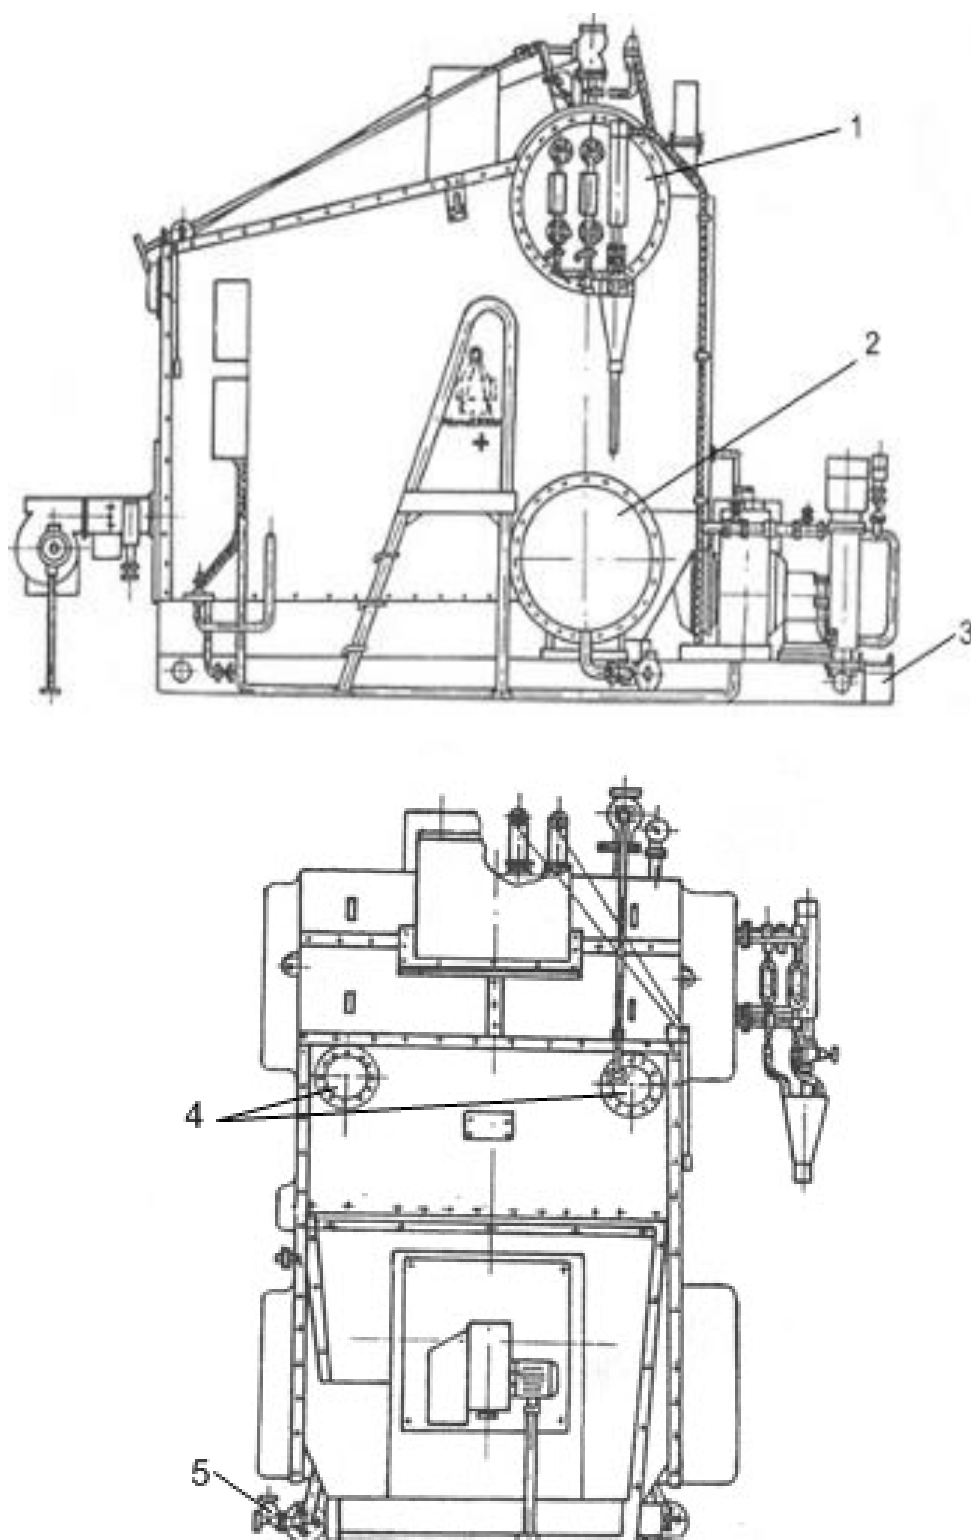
Схема парового котла Е-1,0-0,9Г: 1-верхній барабан; 2-нижній барабан; 3-опорна рама; 4-верхній колектор; 5-продувні труби
